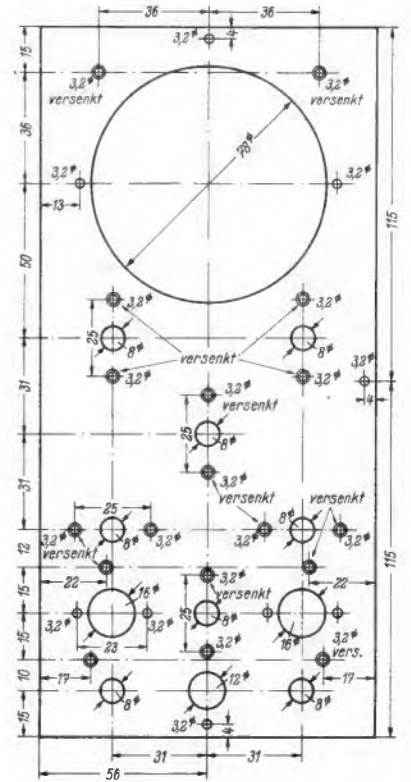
Frontplatte des Oszillografen; Material: 2-mm-Aluminiumblech
